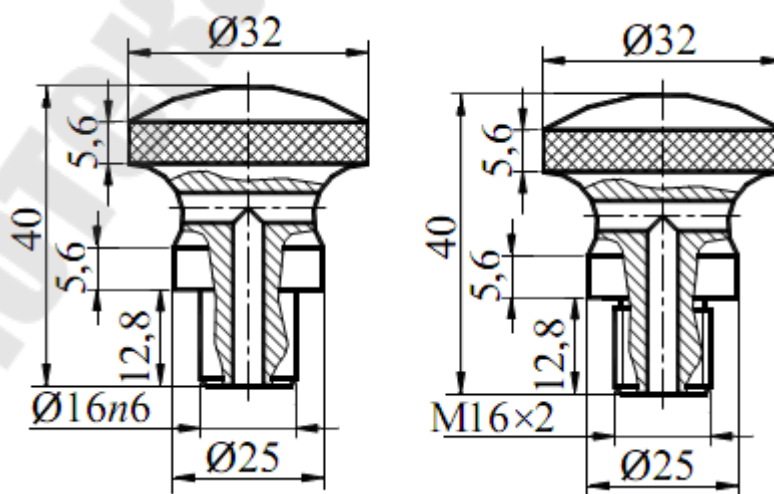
Пробка - отдушина с рукояткой крышки люка
